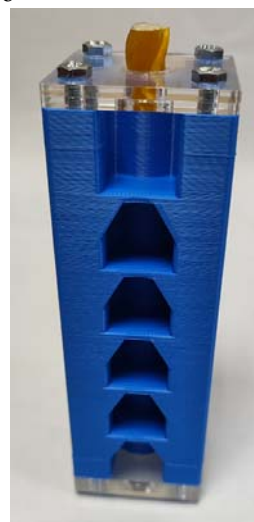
Опалубка для изготовления стеклопластикового болта:
